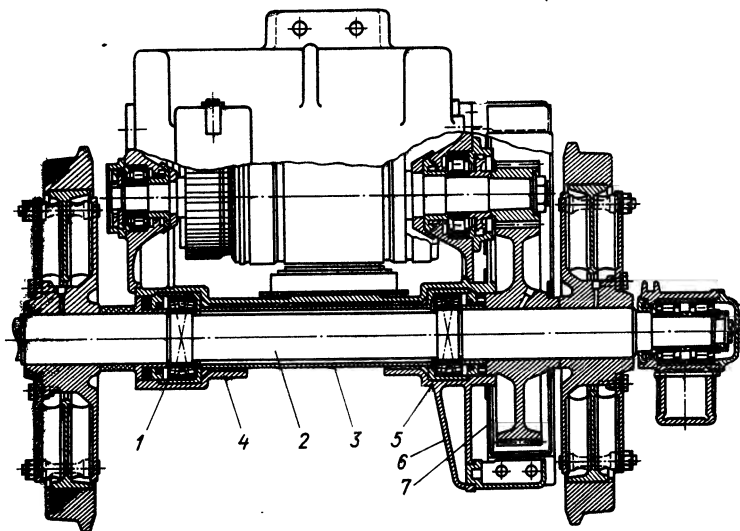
Моторно-осевая подвеска с роликовыми подшипниками
